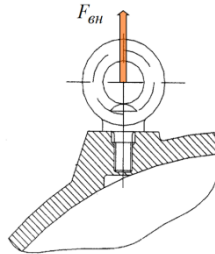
Рымболт, нагруженный осевой растягивающей силой
